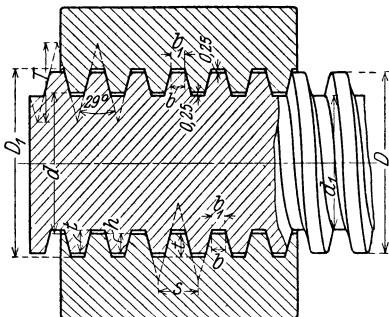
Trapezgewinde mit 29° Flankenwinkel. Fig. 16. Trapezgewinde mit 30° Flankenwinkel.
